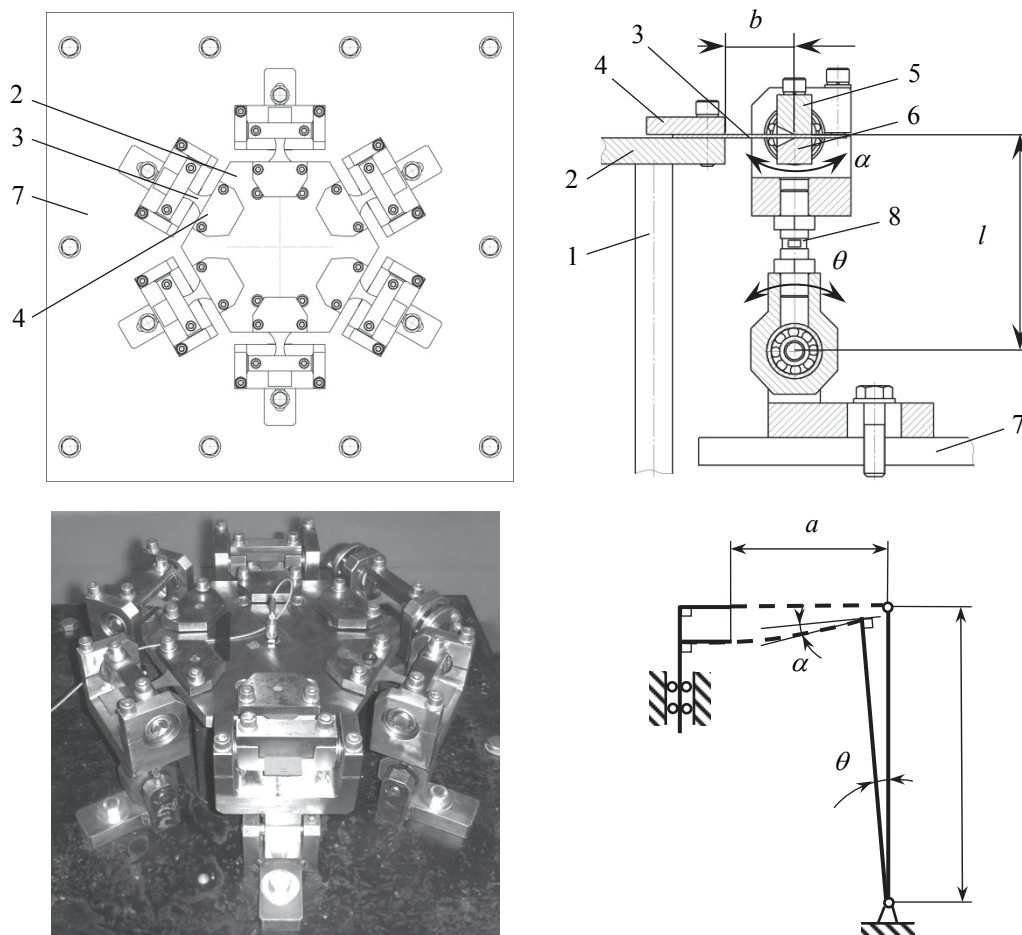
Конструктивная и кинематическая схемы нагрузочного приспособления, реализующего поперечный изгиб консольно зажатых образцов
